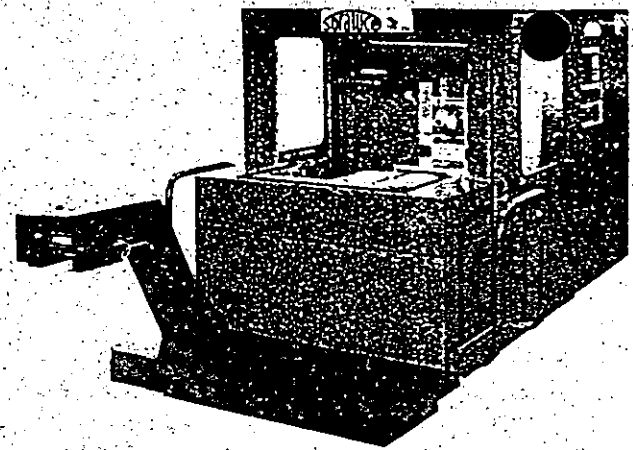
Centro de Maquinado Horizontal Mca. "SORALUCE" Mod. CMH-45, d. 15 Kw., equipado con almacén de 30 herramientas con ISO-40, intercambiador automático de Pellets y mesa giratoria gobernada con CNC como el 4º eje. Dimensiones de la pieza a maquinar, 400x400x400. Control Numérico SIEMENS ó FAGOR. Comercializado y distribuido por DANOBAT MEXICANA.
